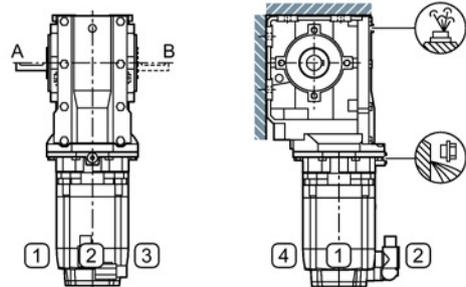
Einbaulagen für Flachgetriebe FZAD und FDAD, Aufsteckausführung, Baugrößen 39 - 129, 2-stufig und 3-stufig
